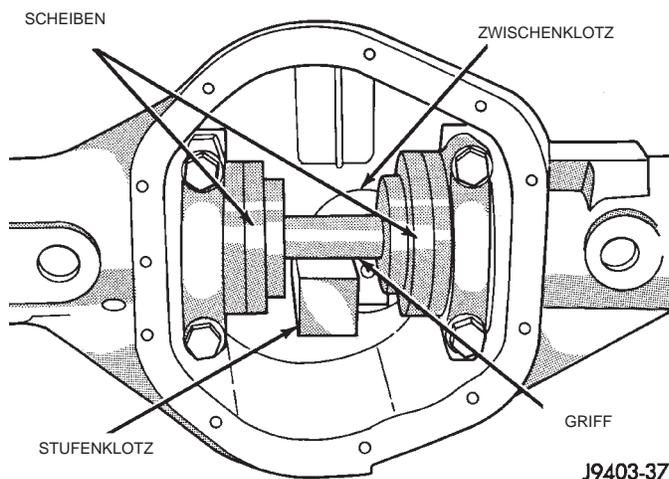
Meßwerkzeuge im Gehäuse eingebaut
